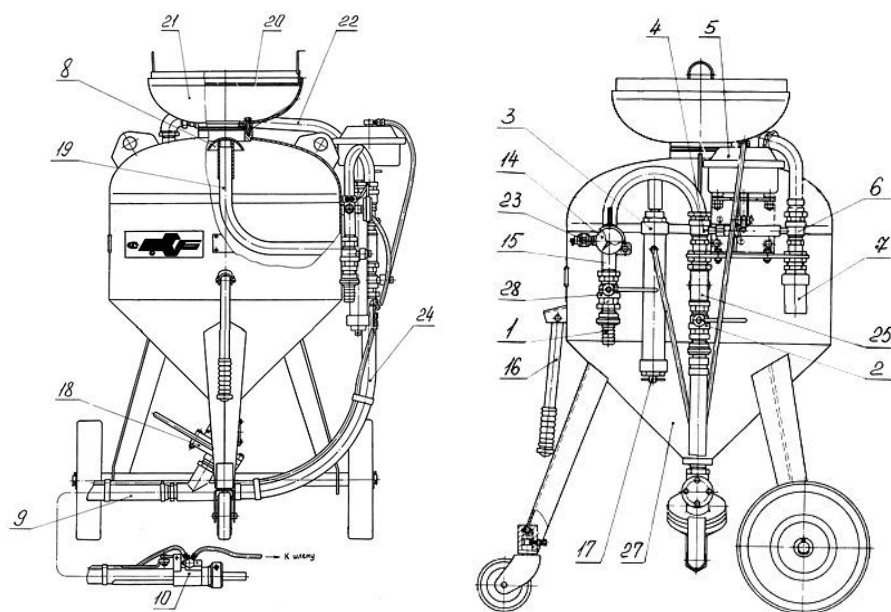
Схема аппарата струйно-абразивной очистки АСО-150. [38].
